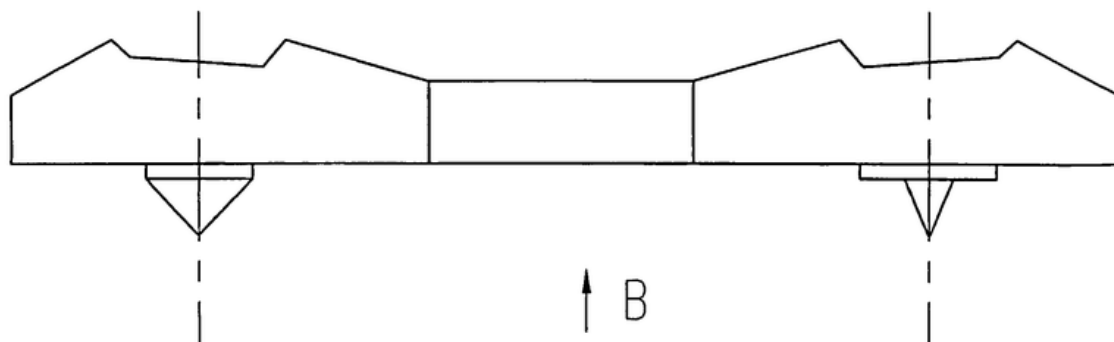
Конструкція рейкової опори із зубатими виступами
